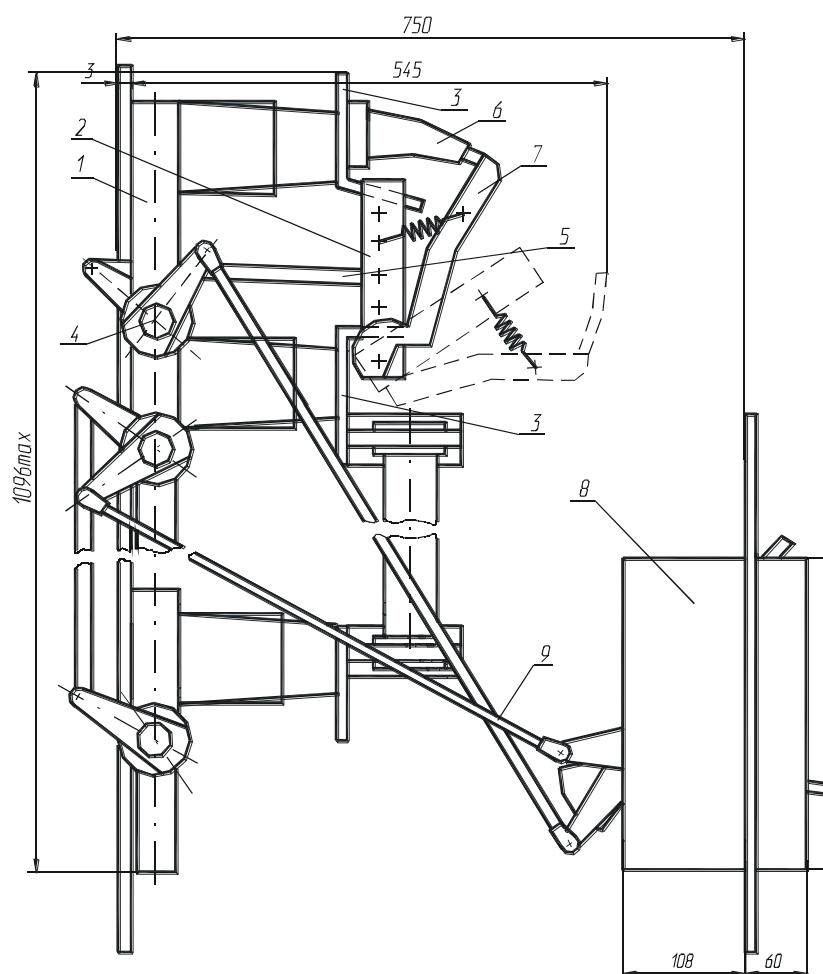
Выключатель нагрузки ВНМ-10 с предохранителями и спаренными ножами заземления снизу с приводом ПП-16 в камере КСО-301
